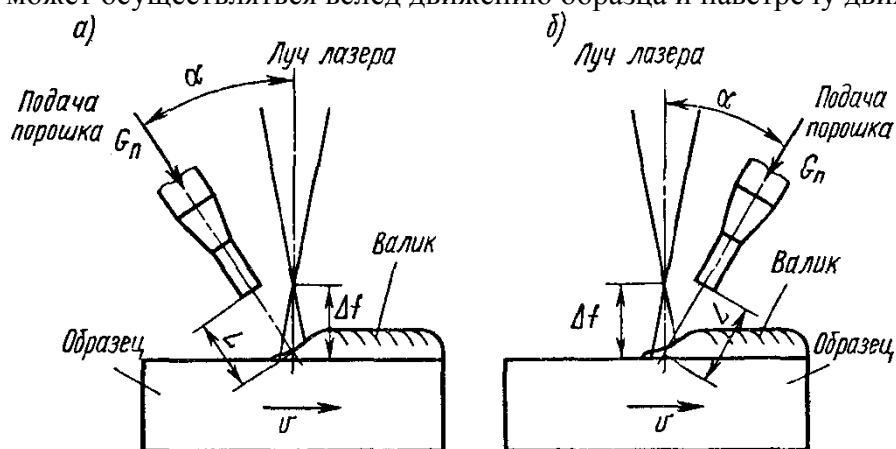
Схема газопорошковой лазерной наплавки с подачей порошка вслед движению (а) и навстречу движению образца (б)
